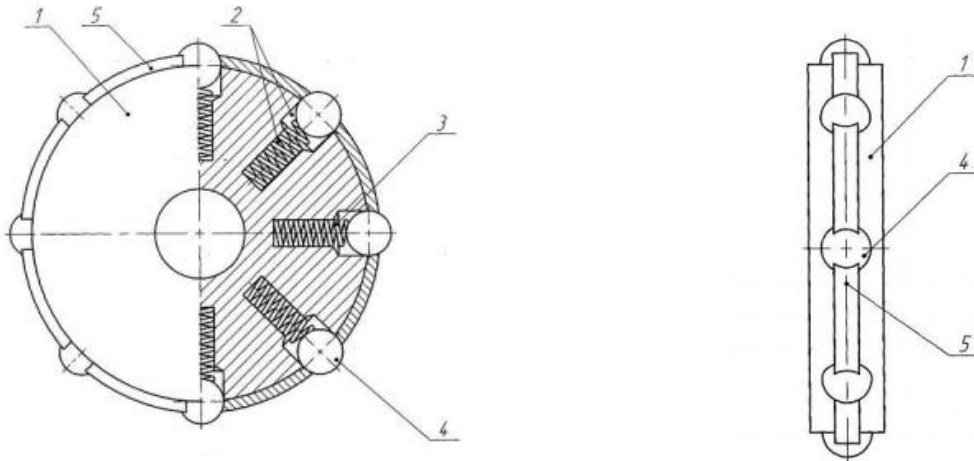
Інструмент для розкочування та зміцнення внутрішньої циліндричної поверхні кульками (Патент 63795)
